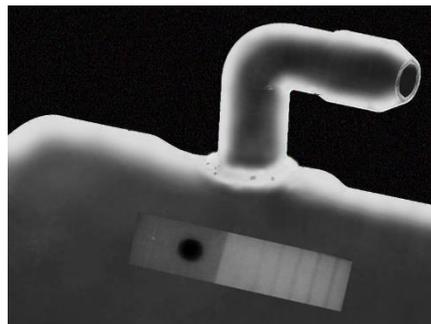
Рентгенограмма сварного шва в месте соединения цилиндра со штуцером
